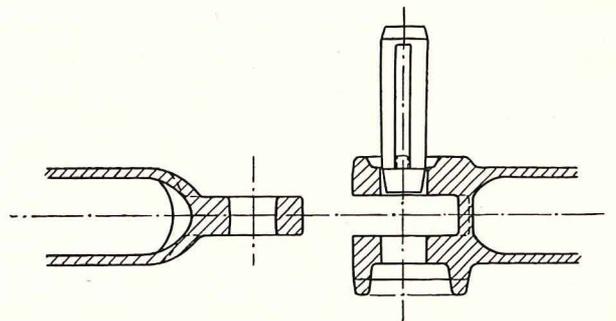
Vue des deux extrémités de la béle et de l'axe d'assemblage.
